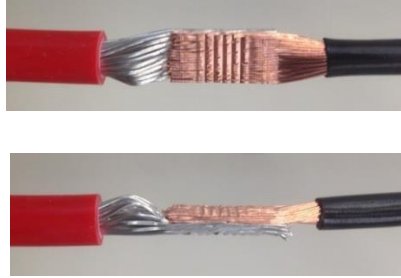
Presença de loops no cabo de alumínio causados por amplitude excessiva durante a soldadura
